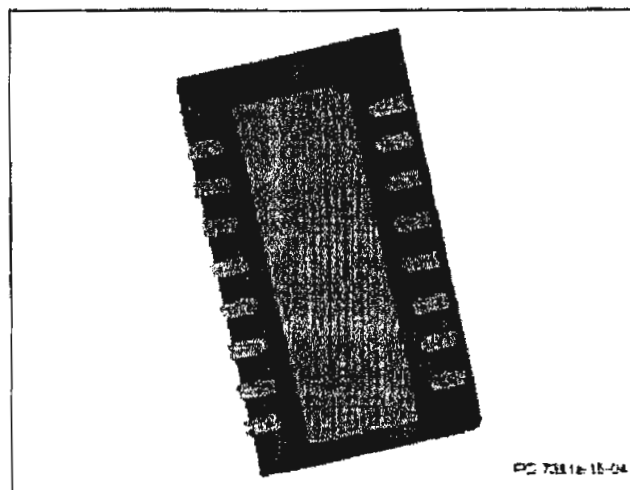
Конструкция безвыводного корпуса с малым контуром (SON)
